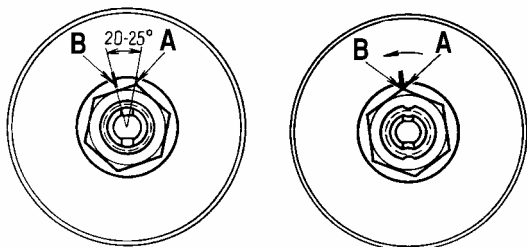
Затягивание и регулировка подшипников ступицы переднего колеса:
